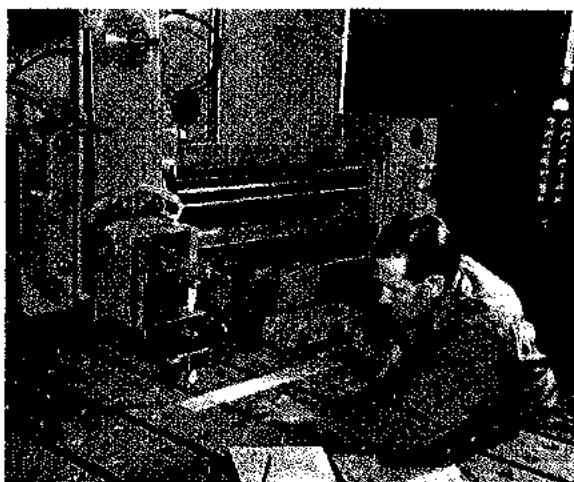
Comparador fijado a la caja de herramientas para comprobar el paralelismo y la perpendicularidad del puente respecto a la mesa (Rockford Machine Tool Co.)
